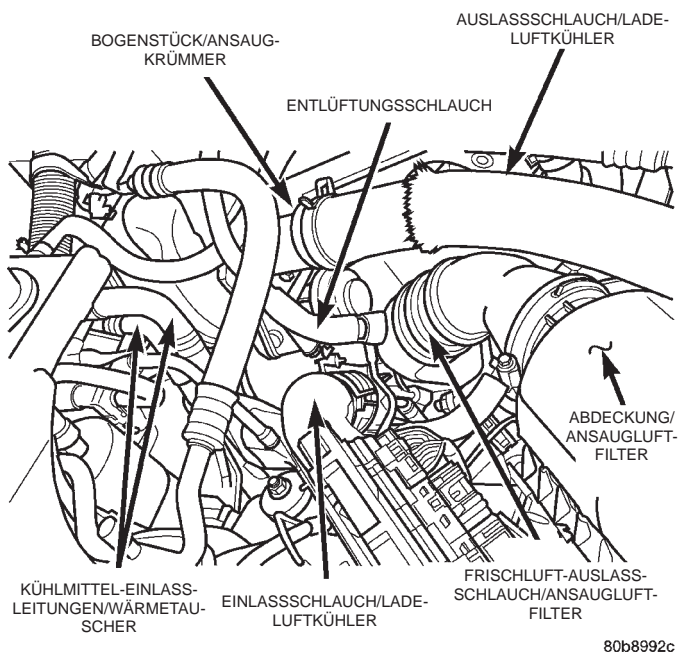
Motorraum—Linksgelenkte Fahrzeuge mit Dieselmotor
